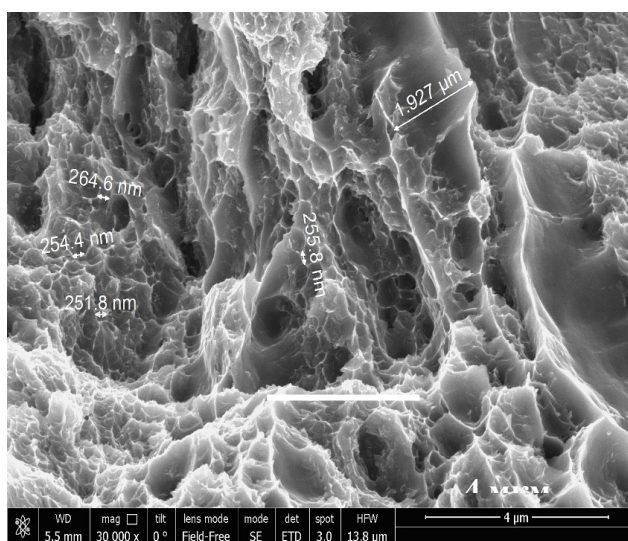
Вид ямок вязкого излома на поверхности разрушения образца.
